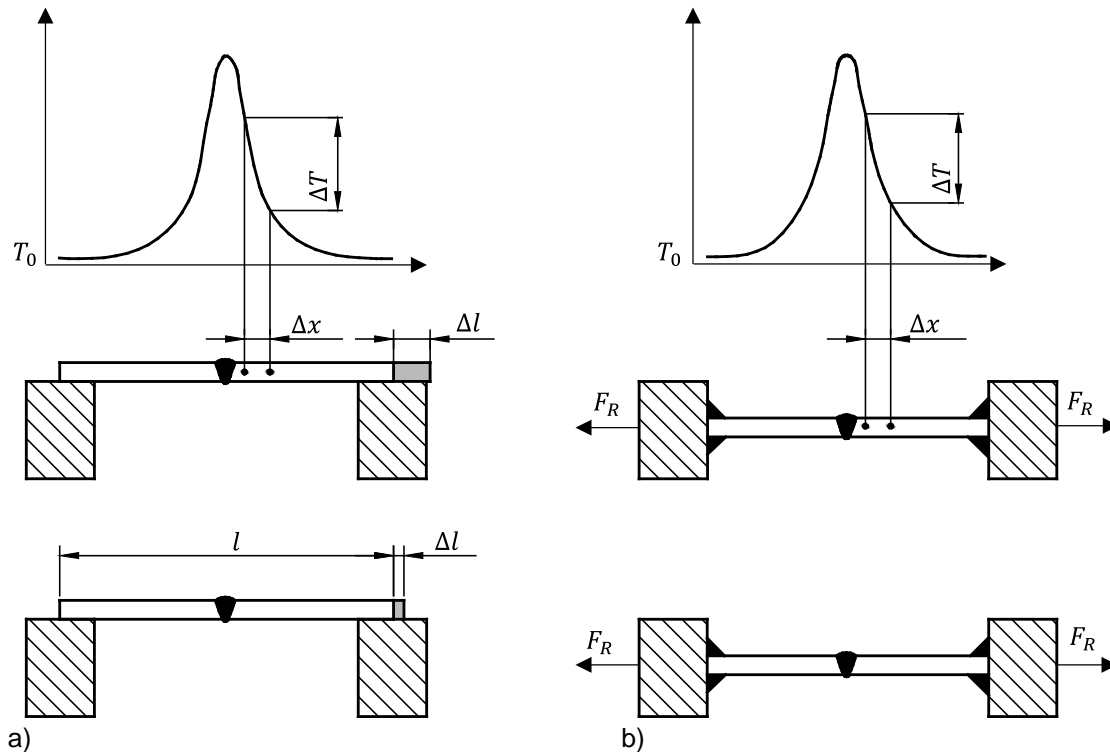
Behinderte Ausdehnung einer geschweißten Verbindung nach [2].
